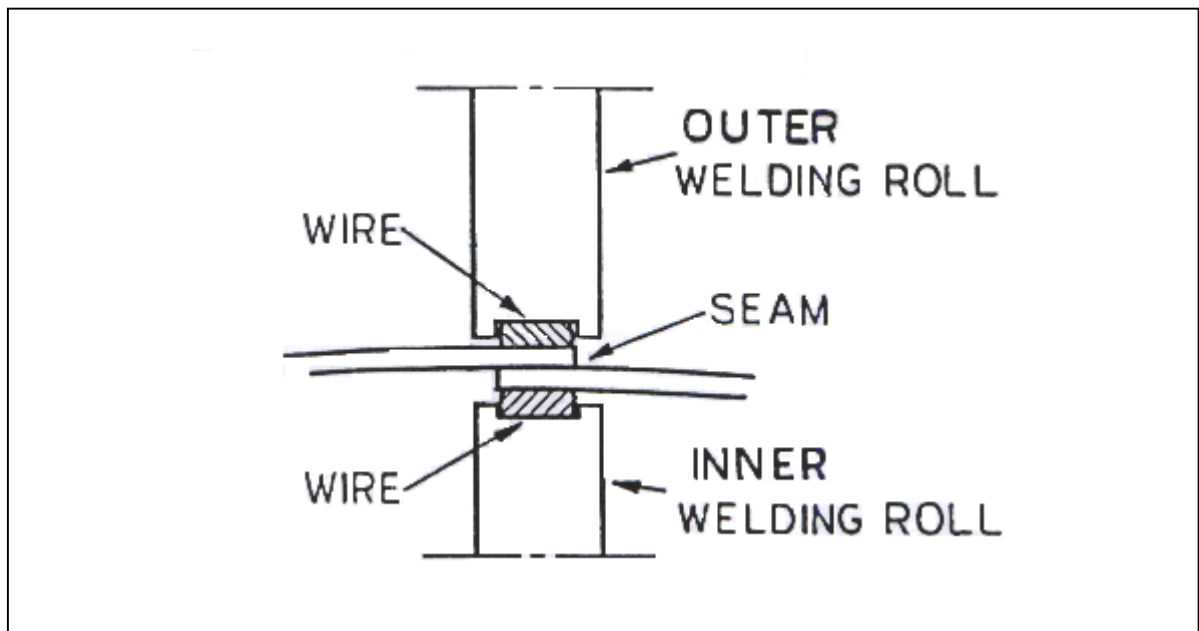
Sección de cruce de la estación de soldadura
